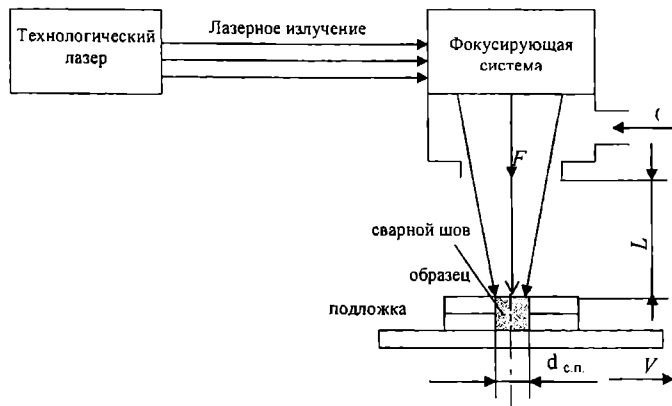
Схема и обозначение параметров, обеспечивающих процесс лазерной сварки текстильных материалов:
